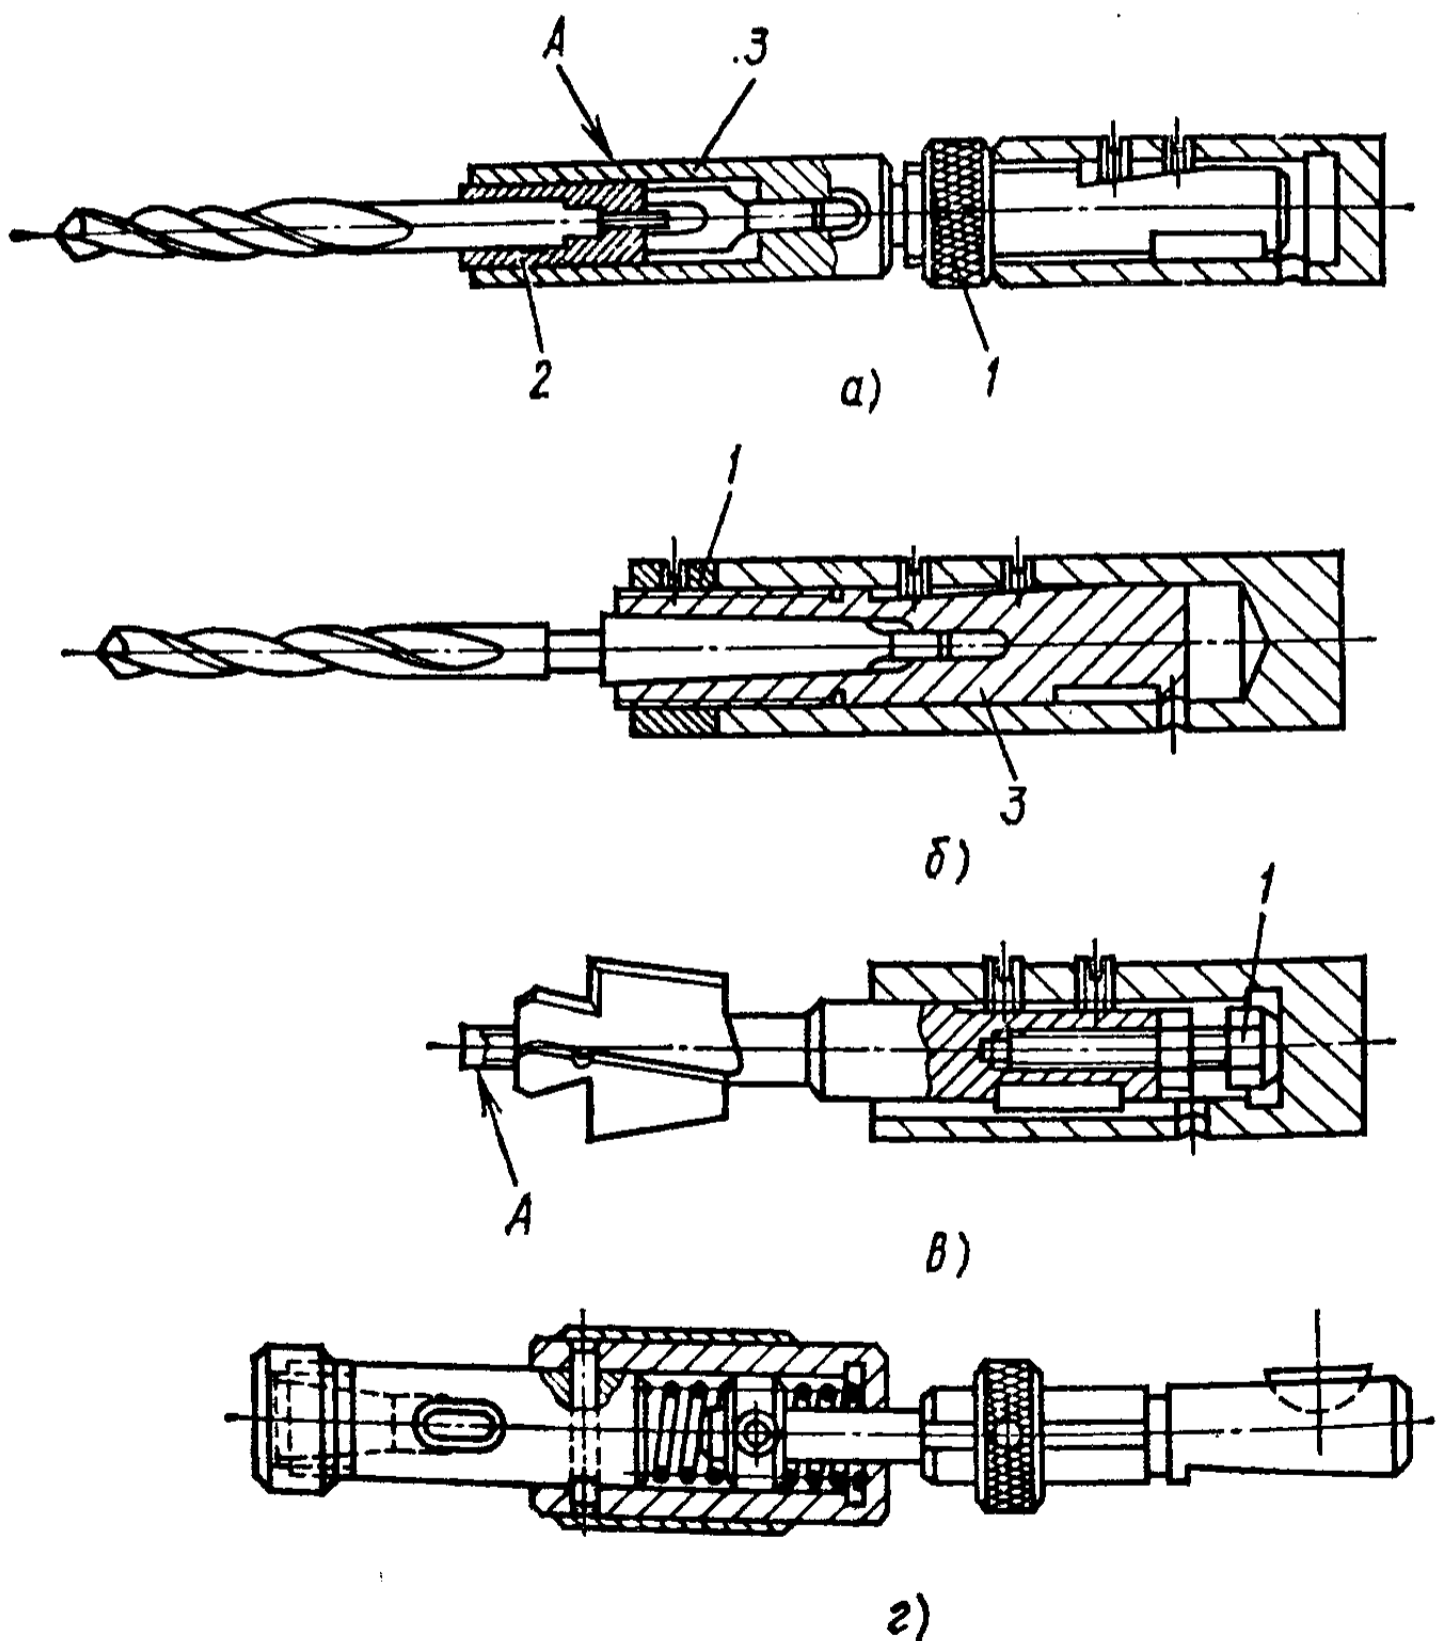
Вспомогательный инструмент агрегатных станков (А — направляющие участки)
